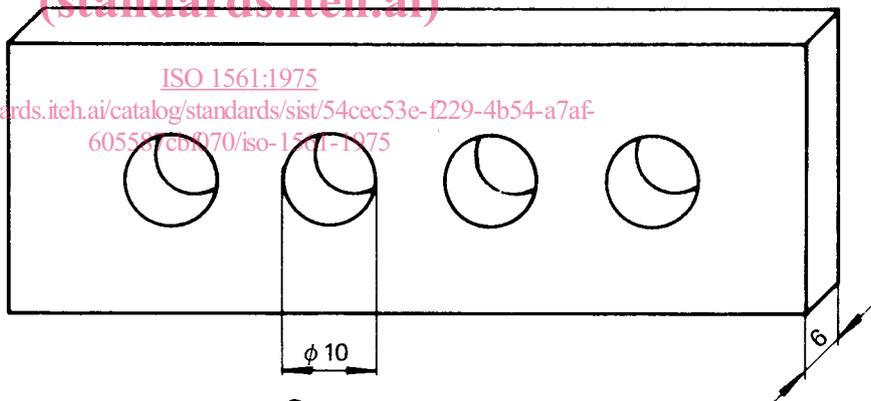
Moule pour la préparation des éprouvettes pour l'essai de fluage
